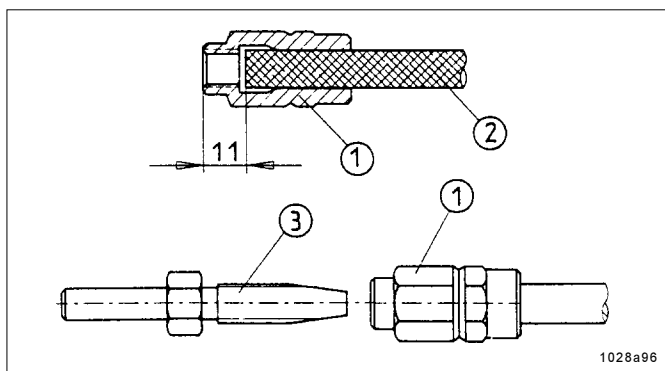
Vormontage der Schraubhülsen und Schlauchstutzen auf die Hauptleitung
